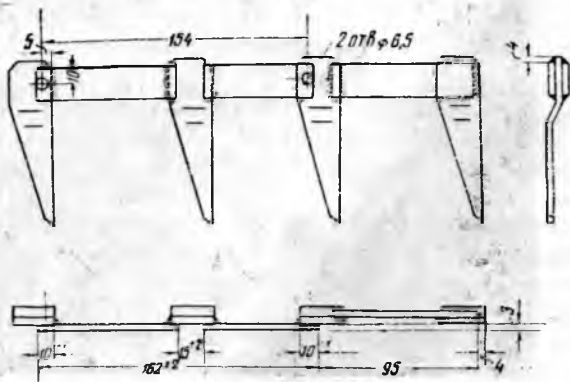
Съемное приспособление ЦНИИМЭ СК-1
